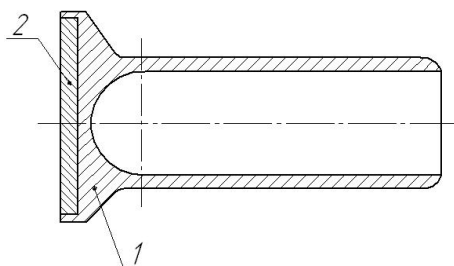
Общий вид биметаллической детали — толкатель клапана ДВС автомобиля «КамАЗ»:
